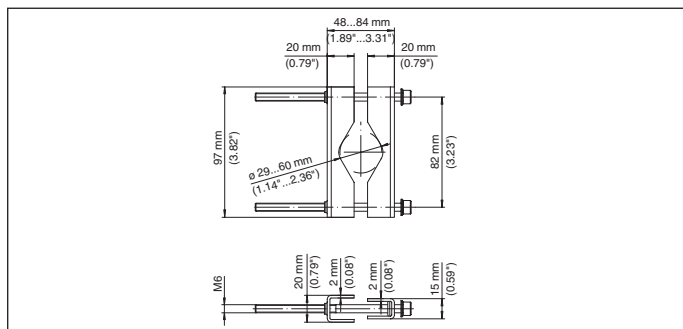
Afmetingen klemmen voor pijpmontage VEGAMET 861, 862
